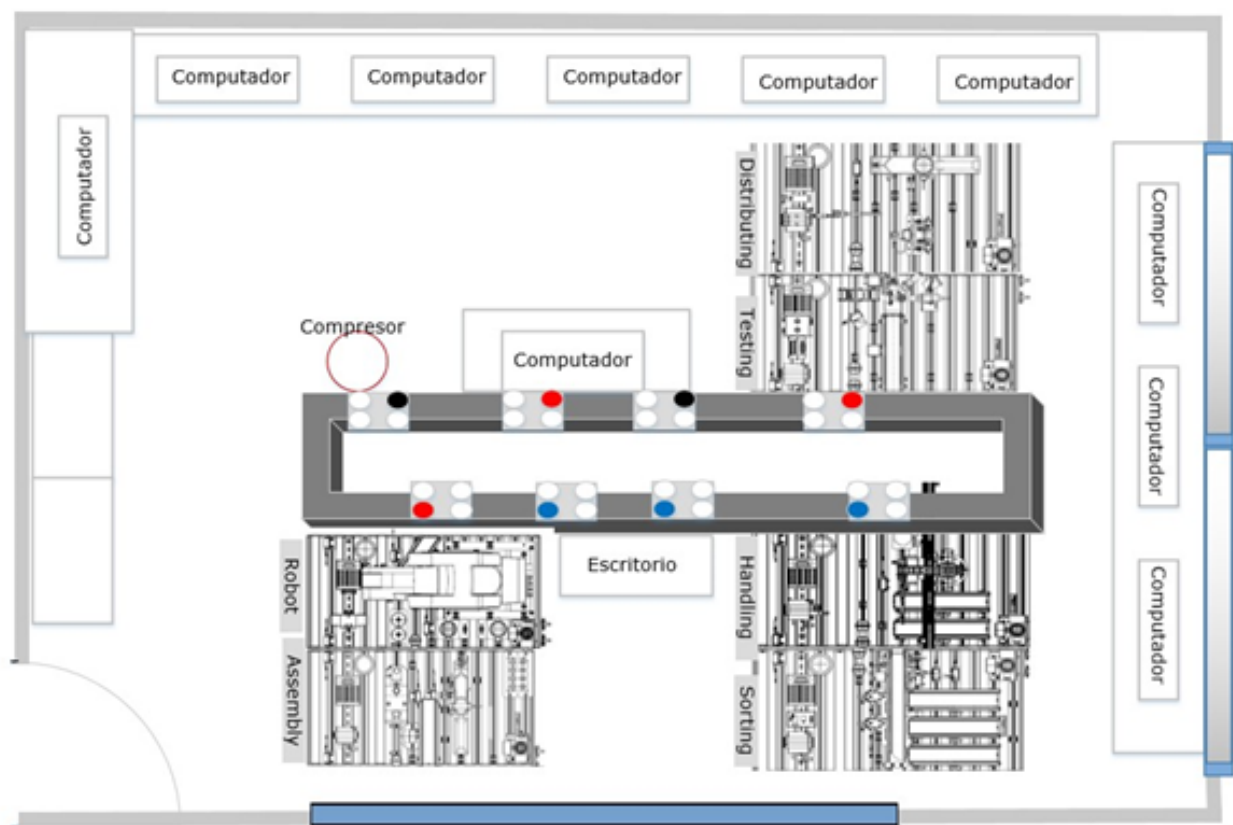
Sistema Integrado de Manufactura de la Fundación Universitaria Los Libertadores
